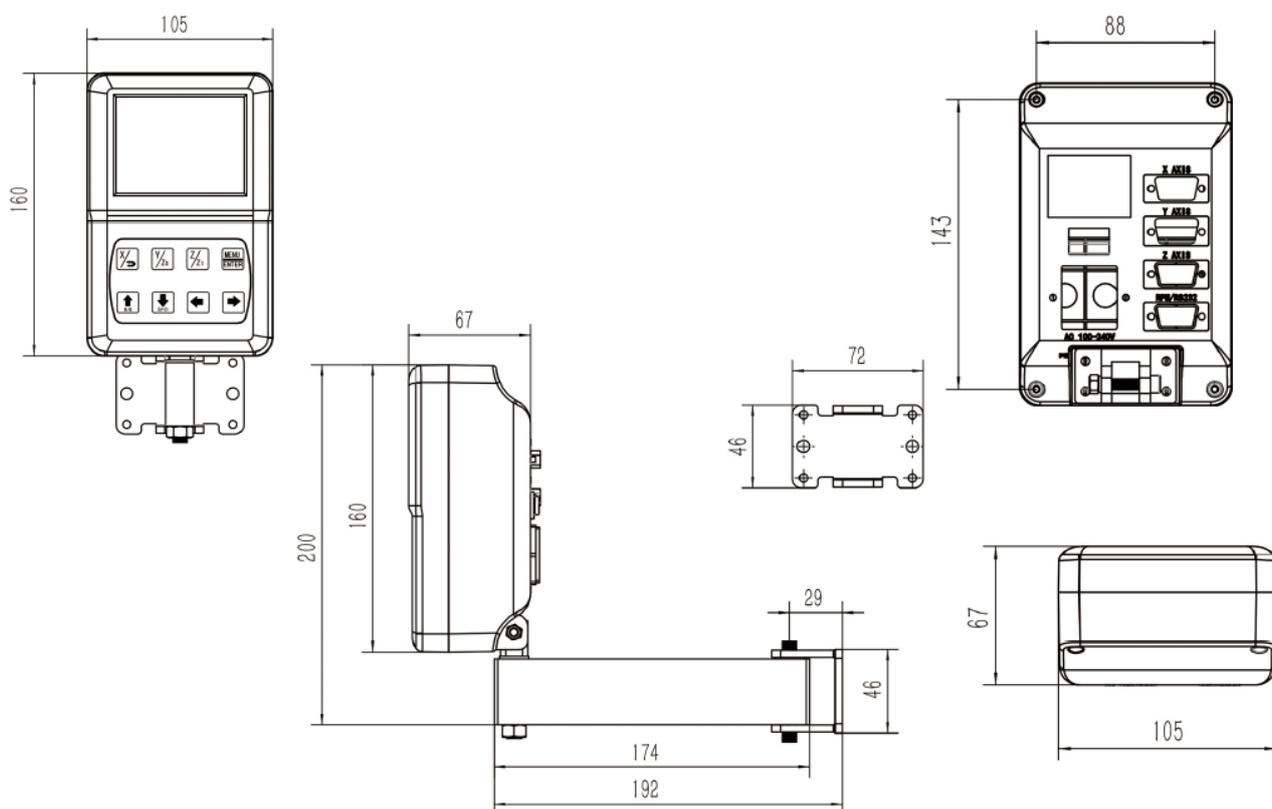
Габаритный чертеж цифрового дисплея D50.
